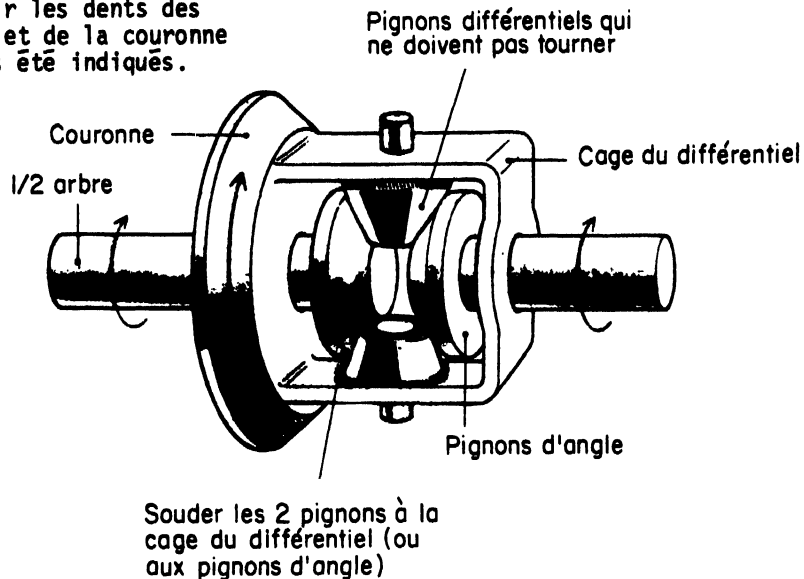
BLOCAGE DU DIFFERENTIEL PAR SOUDURE
